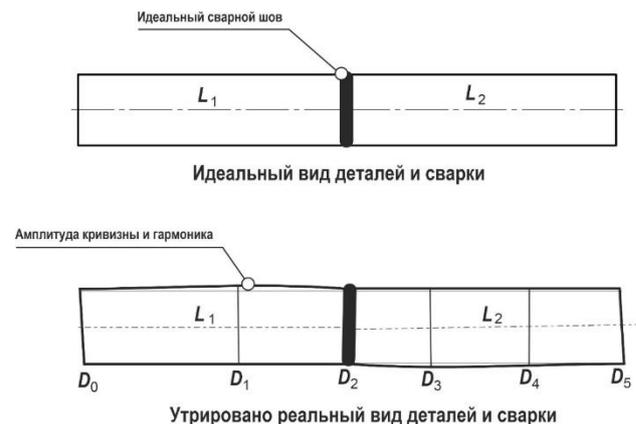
Идеальный и реальный виды деталей и сварки
